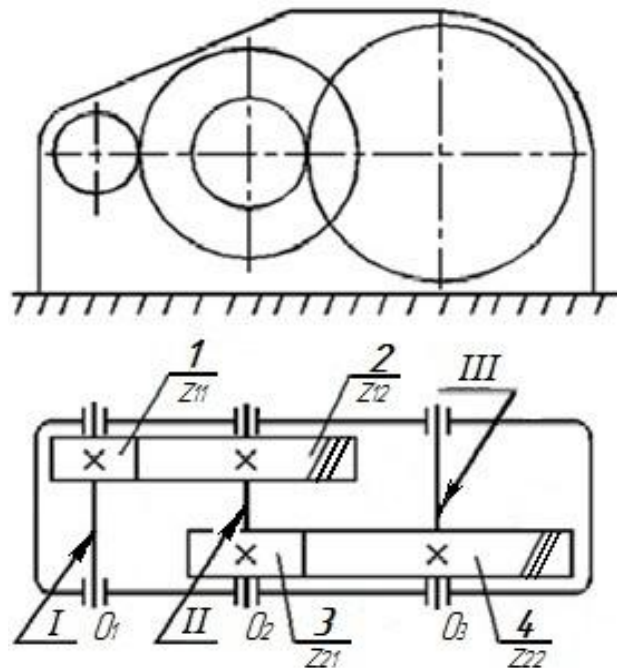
Схема цилиндрического двухступенчатого редуктора:
